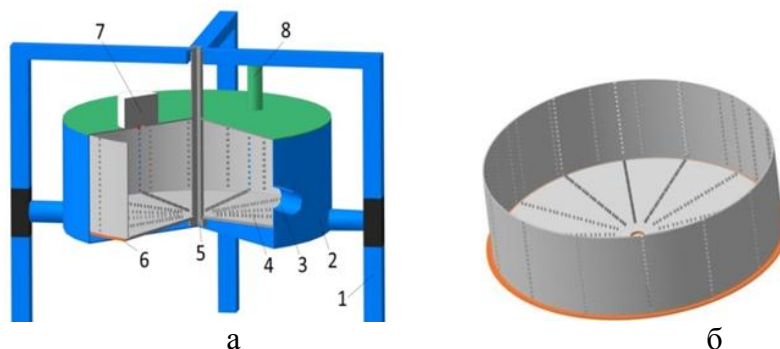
СВЧ установка с коаксиальным резонатором:
